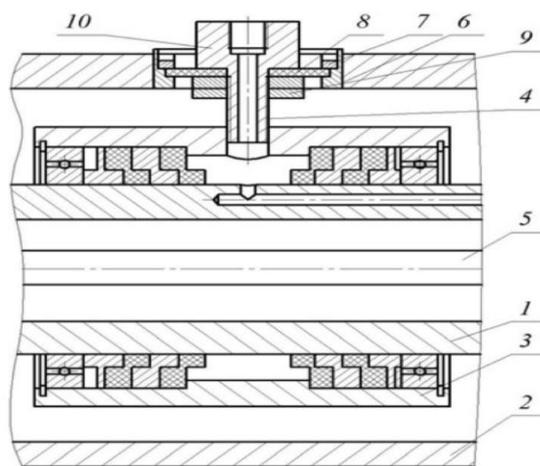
Крепление блока уплотнителей: 1 – цапфа колеса; 2 – ступица; 3 – подшипник; 4 – блок уплотнителей; 5 – полуось; 6 – эксцентриковая втулка; 7 – кольцевая гайка; 8 – диафрагма; 9 – гайка; 10 – переходник.
